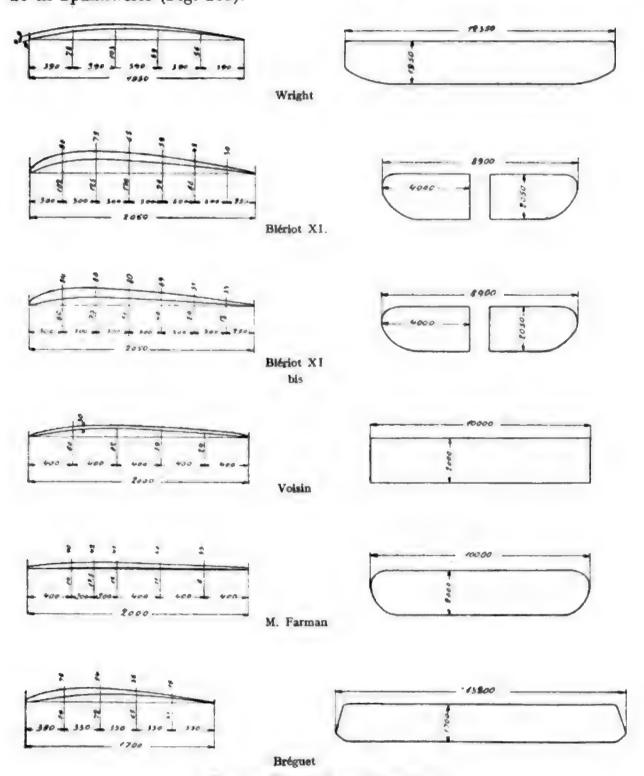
Flügelprofile und -Grundrisse.
